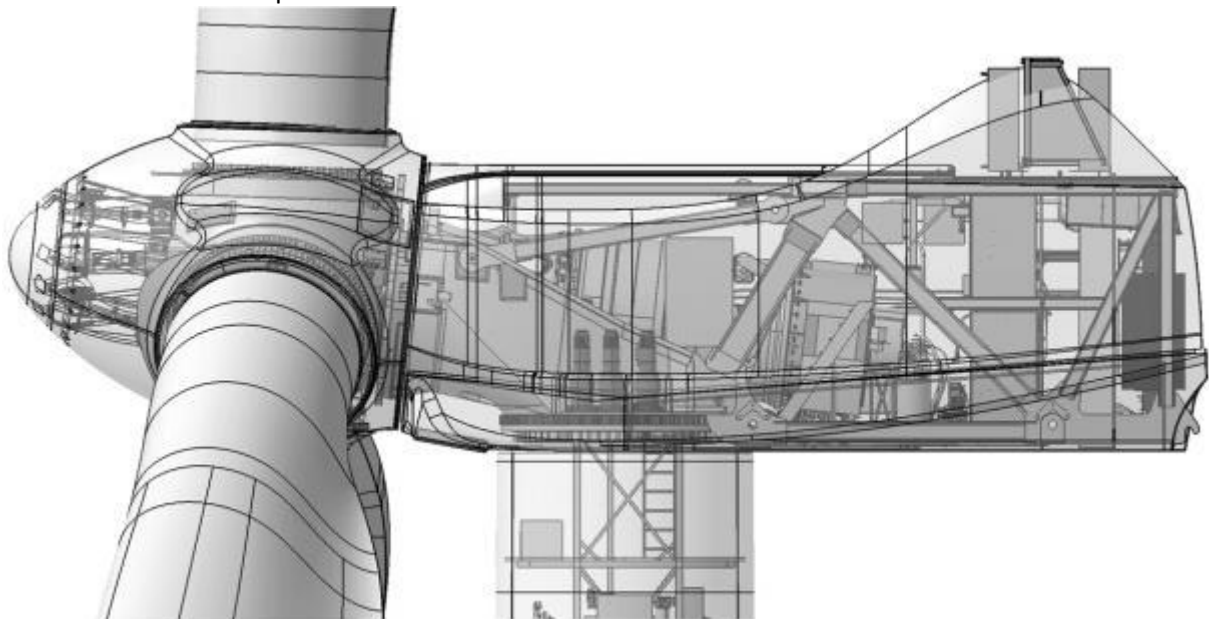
Vista laterale della struttura della Siemens-Gamesa-3,465 MW
